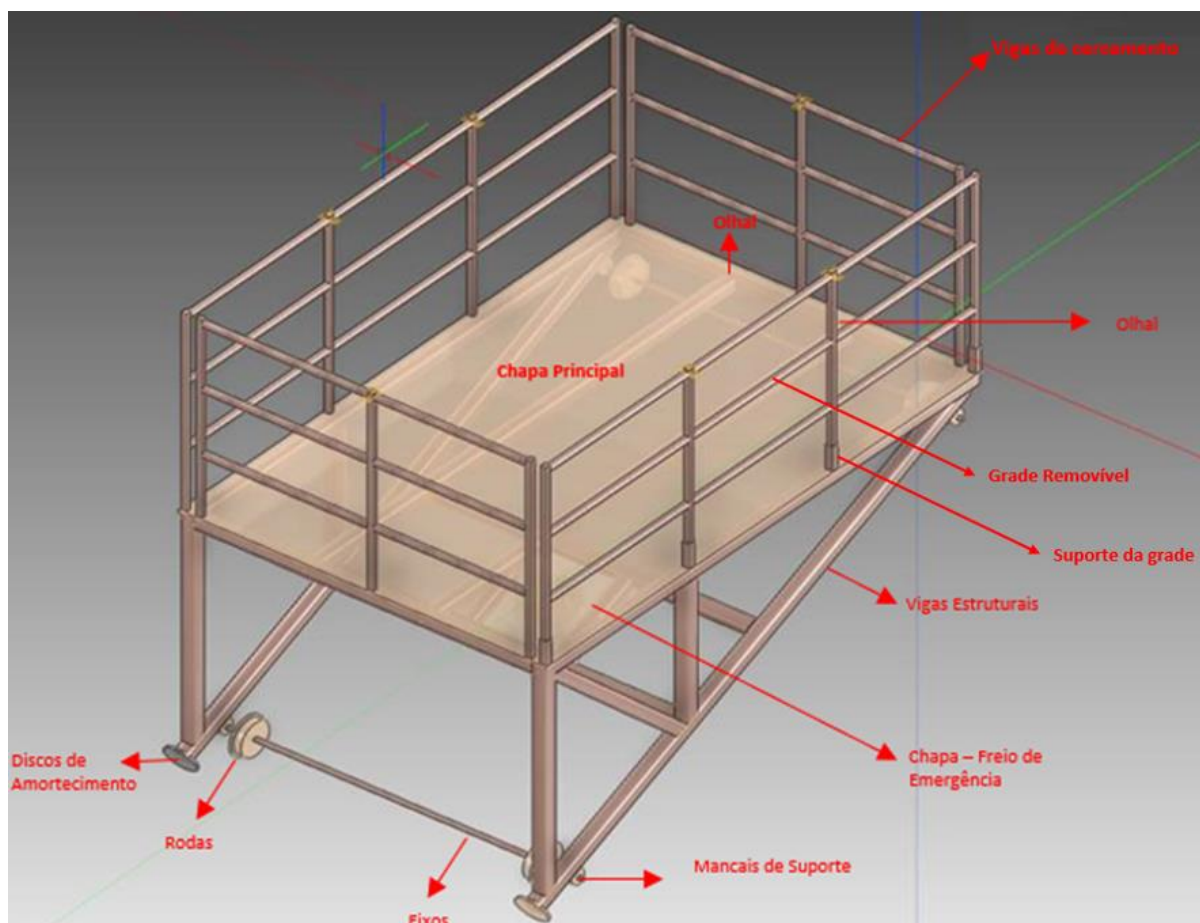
Modelo 3D – AVEVA da estrutura do elevador de plano inclinado
